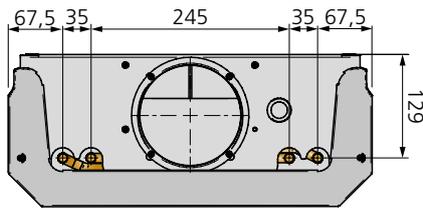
Dimensions ADRIATIC Prisma, vue arrière du raccordement hydraulique
